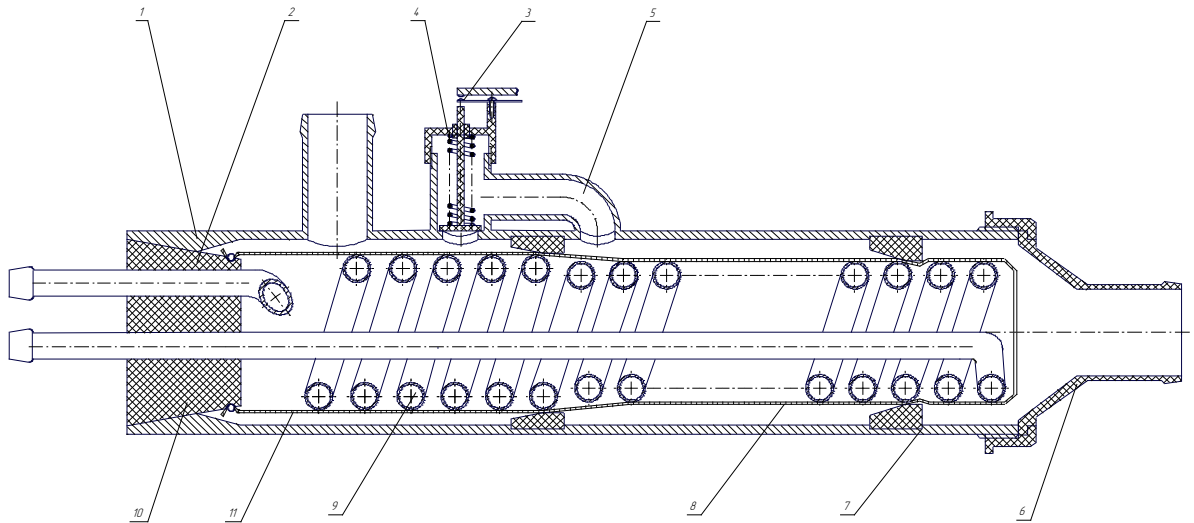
Схема вакуумного молочного фільтра-охолоджувача : 1- корпус; 2-штуцер що,підводить молоко; 3-контакти; 4 - запобіжний клапан; 5-обвідний патрубок; 6-вихідний патрубок; 7,8-кільця ущільнювачів; 9-змесвик-охолодник; 10 - пробка
